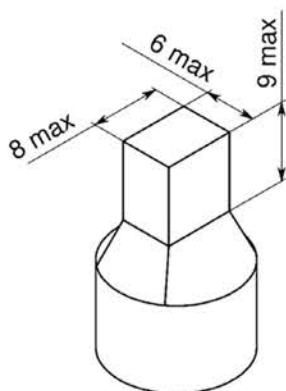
Форма и размеры проводника, подготовленного для присоединения к АВДТ
